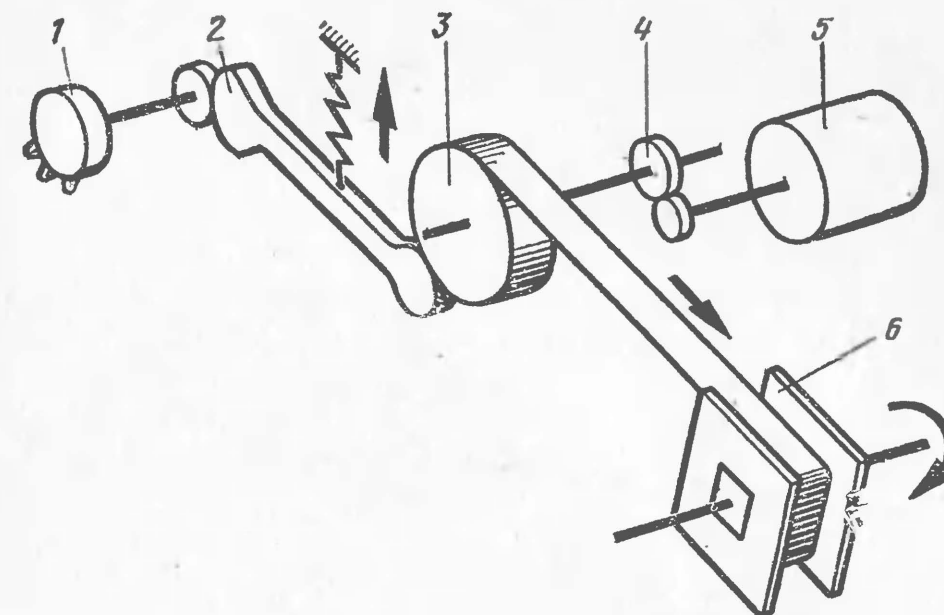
Кинематическая схема механизма натяжения намоточного станка
